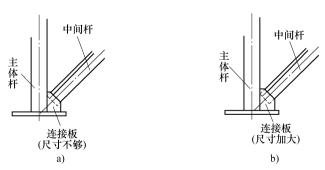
修正结构尺寸 a) 改动前连接板尺寸不够 b) 改动后加大连接板尺寸
